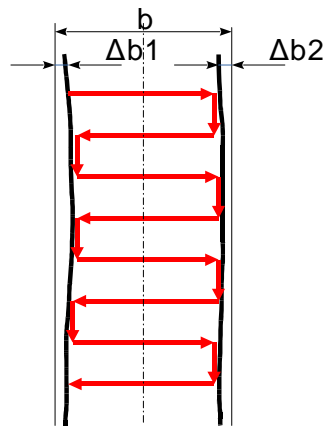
Поперечные колебательные движения электрода при отслеживании медианы сварочного шва в процессе сварки
